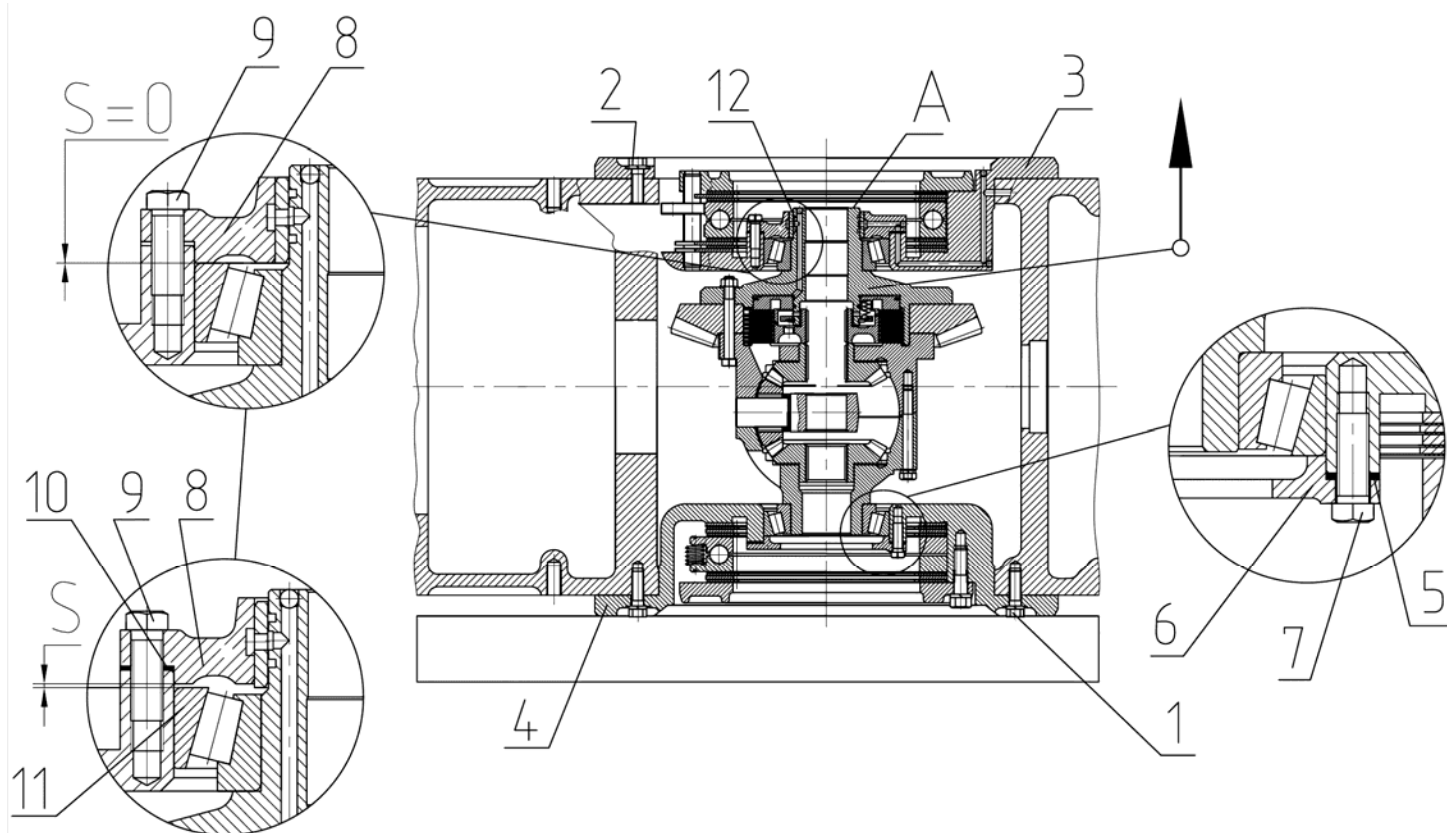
Регулировка осевого зазора в конических подшипниках дифференциала.
